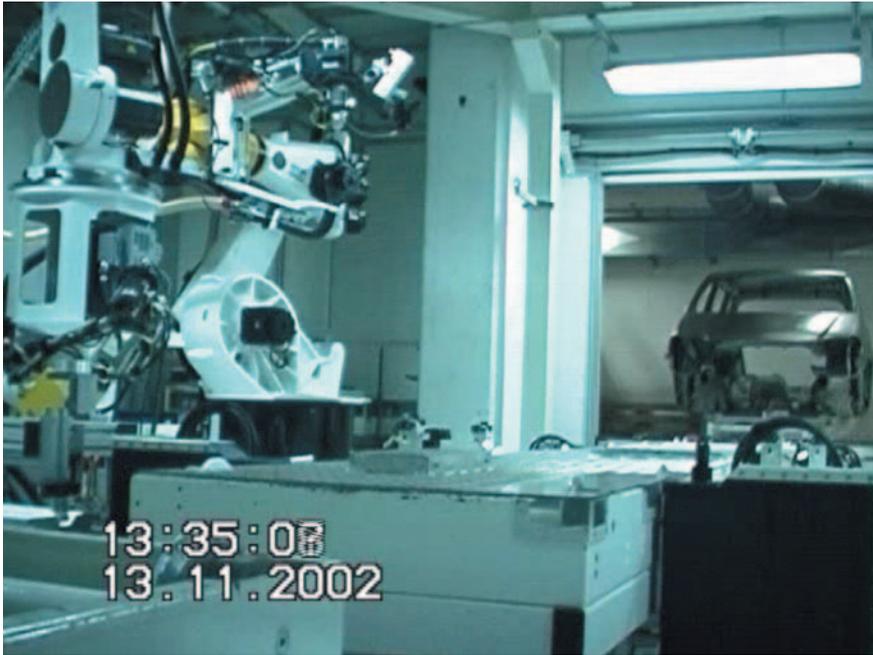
Laserstrahlschneiden und -schweißen in der Automobiltechnik (Video)
